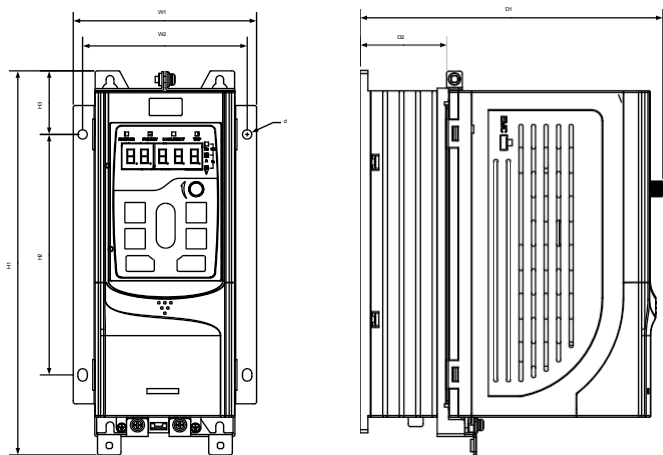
Diagrama de montagem do flange do VFD de 380V 1,5-7,5kW Tabela C-4 Dimensões de montagem do flange do VFD de 380V 1,5-7,5kW (unidade: mm)
